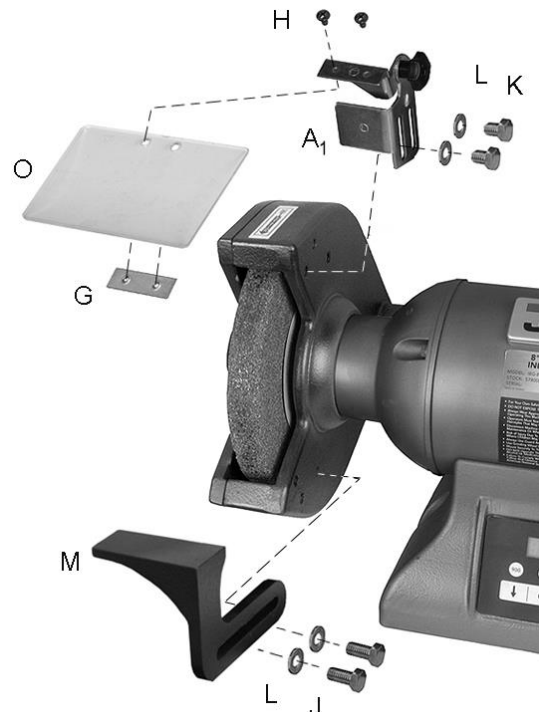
Funkenschutz und Werkzeugauflagen
